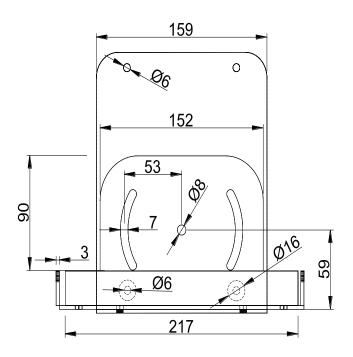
Kit de Montagem AP/Relay - Vista Frontal
